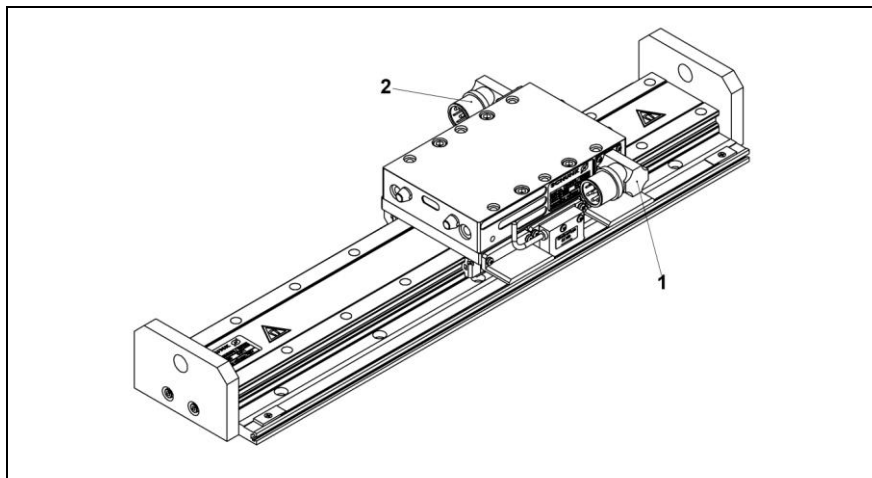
Motorstecker umbauen von Seite 1 auf Seite 2
